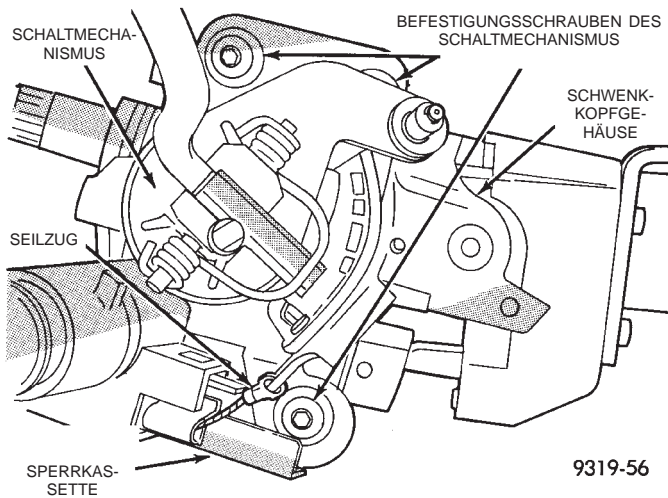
Befestigung des Schaltmechanismus am Gehäuse des Schwenkkopfs
